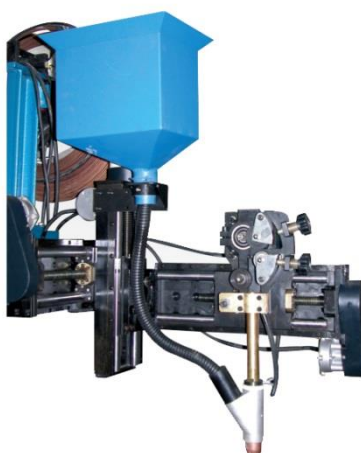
Сварочная горелка NA3-SF
